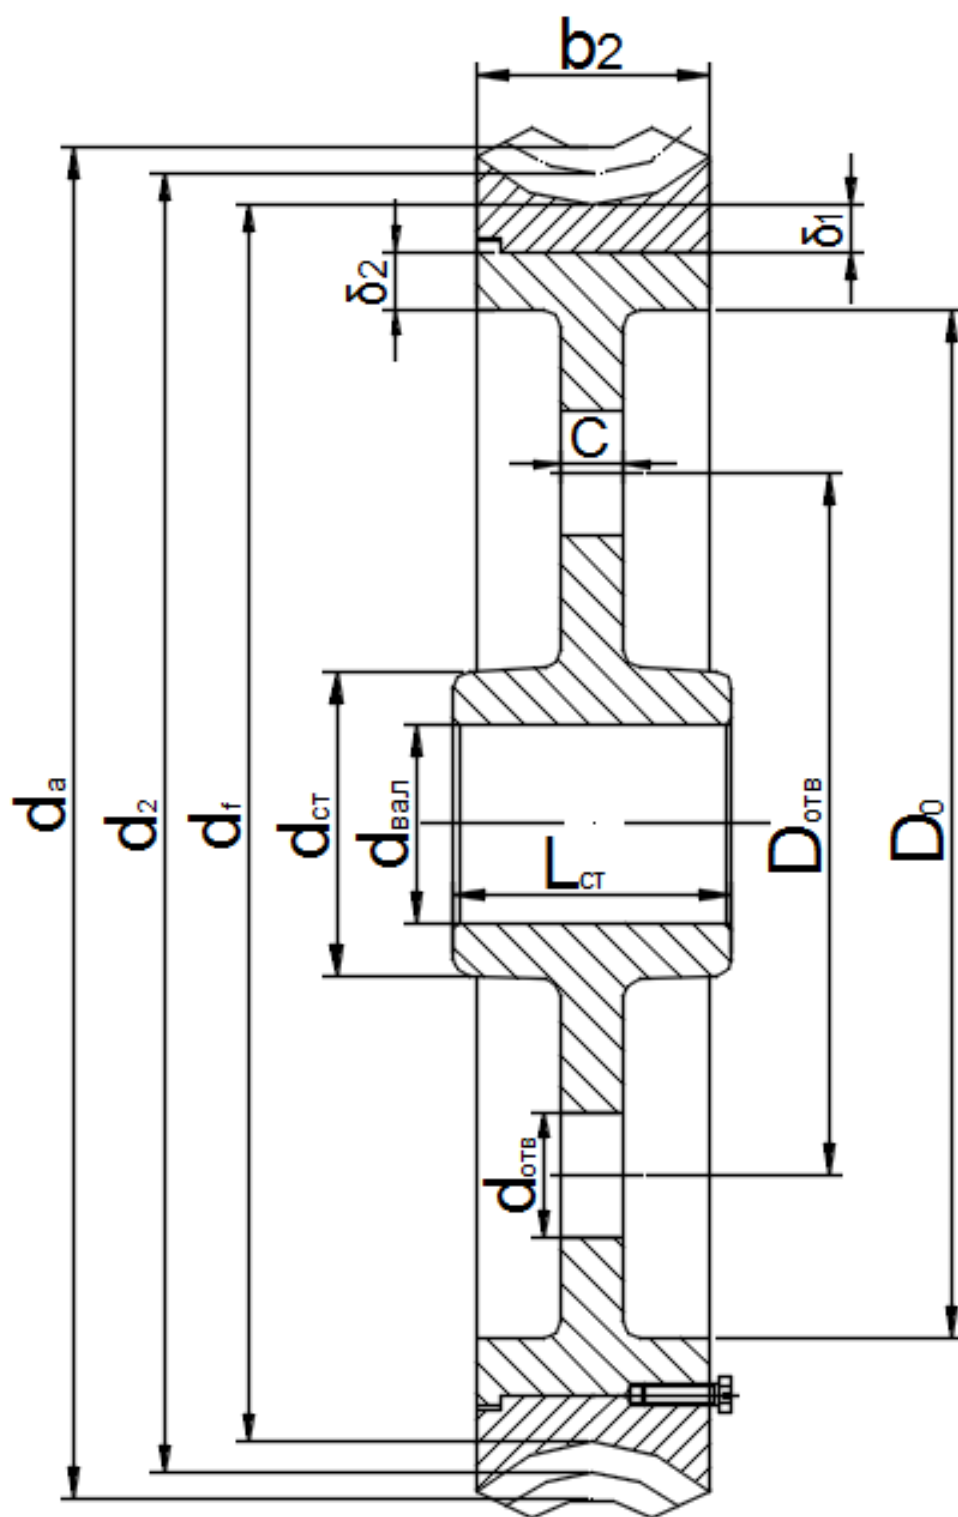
Конструктивные размеры червячного зубчатого колеса
